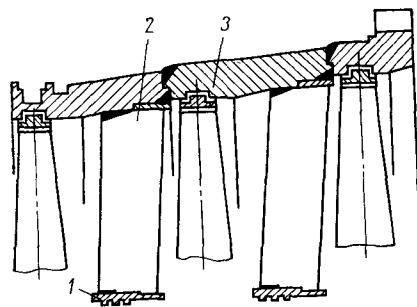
Сварные диафрагмы первой и второй ступеней турбины ГТ-25-700 ЛМЗ:
